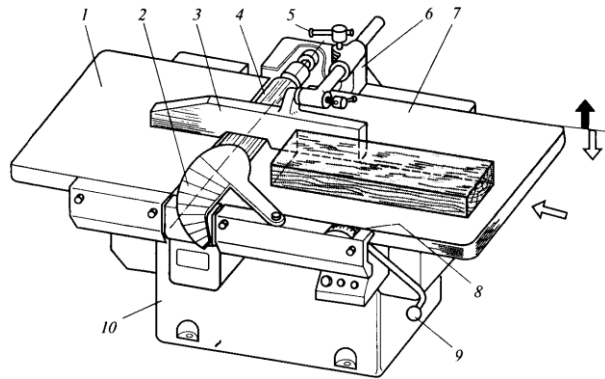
Однобічний фугувальний верстат: 1, 7 – столи; 2 – огороження; 3 – напрямна лінійка; 4 – ножовий вал; 5 – фіксатори кріплення напрямної лінійки; 6 – кронштейн; 8 – шкала; 9 – рукоятка настроювання стола по висоті; 10 – станина
